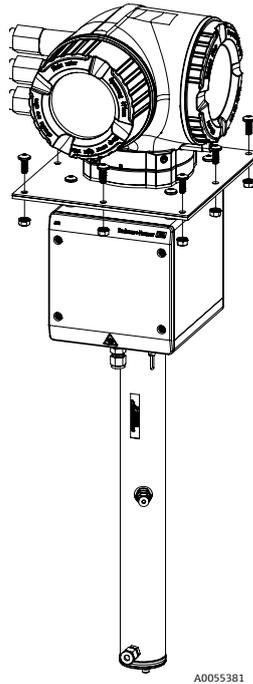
Halterung für Montage auf einem Befestigungsblech und Befestigungsmaterialien für J22
